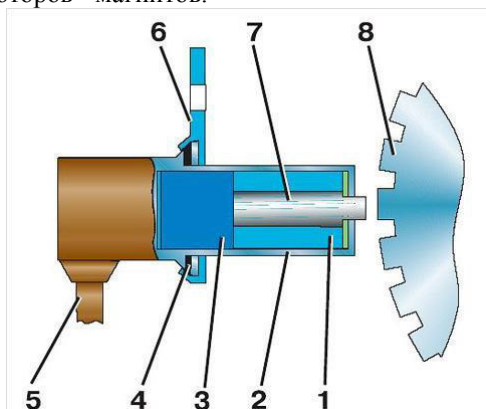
Датчик угла поворота коленчатого вала двигателя:
